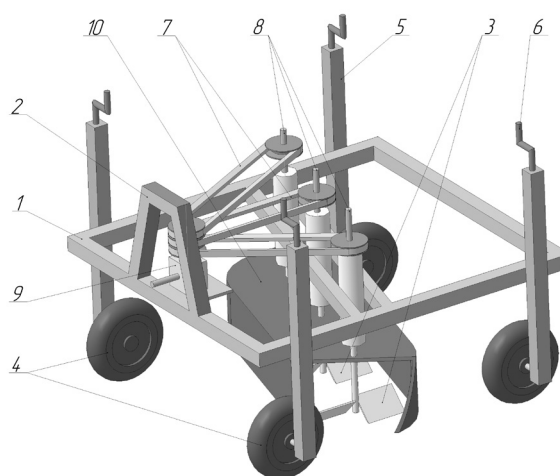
Ботвоудаляющая машина: 1 – рама; 2 – устройство для присоединения к трактору; 3 – рабочие органы; 4 – пневматические колеса; 5 – стойки; 6 – механизм механического регулирования высоты скашивания; 7 – ременные передачи; 8 – валы; 9 – конический редуктор; 10 – кожух
